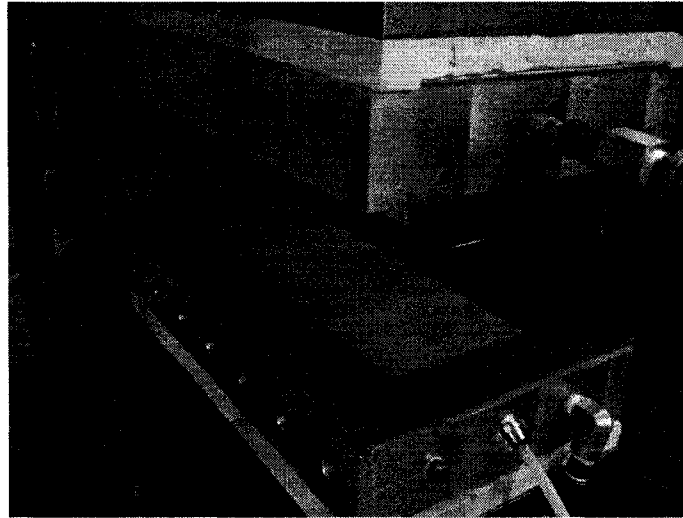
Membrane en silicone conducteur (au centre) avec joint de renforcement sur le plan de joint du moule.
